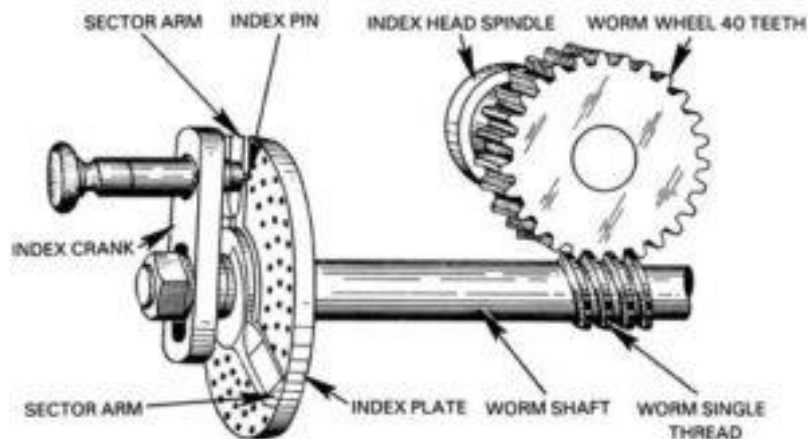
Зовнішній вид звичайної ділильної головки другого типу [16]
